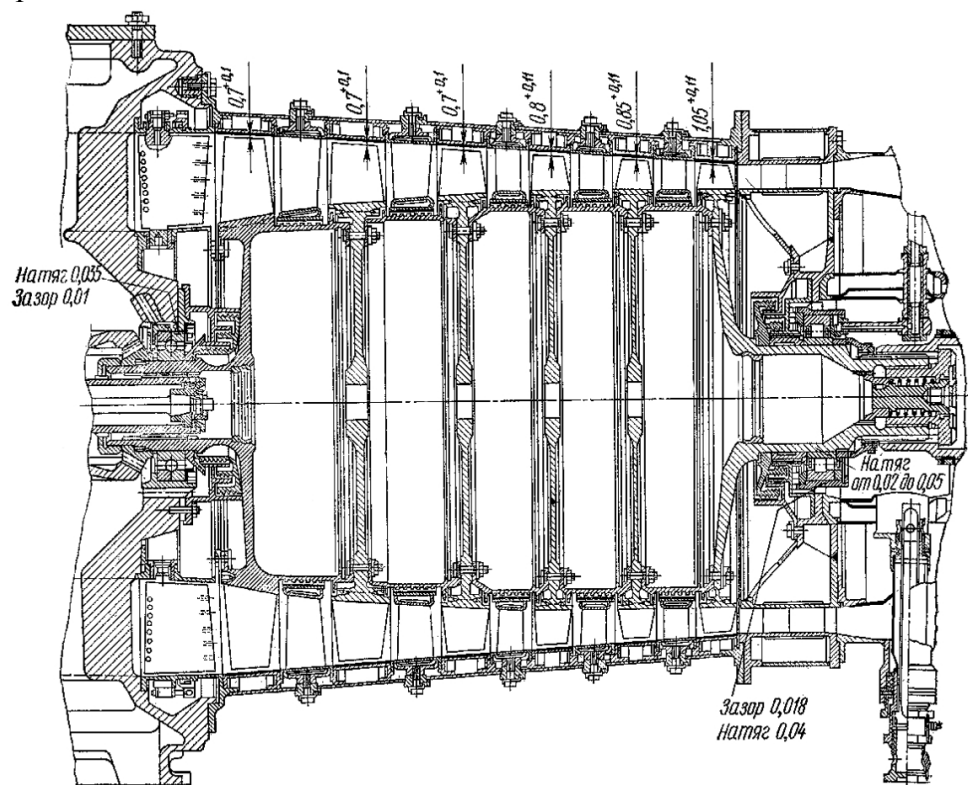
Продольный разрез компрессора ТВД с ротором, секции которого скреплены призонными болтами, и сваренным из листовой стали корпусом.
